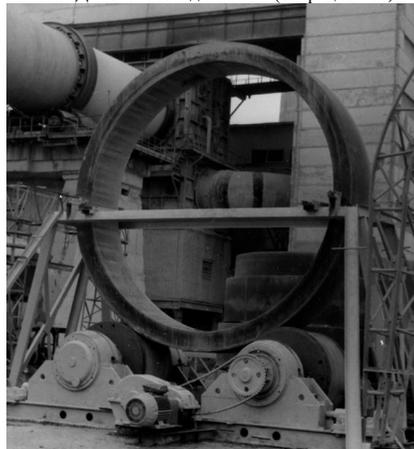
Бандаж, установленный на специальный стенд для обработки торцевых поверхностей (операция 020)
